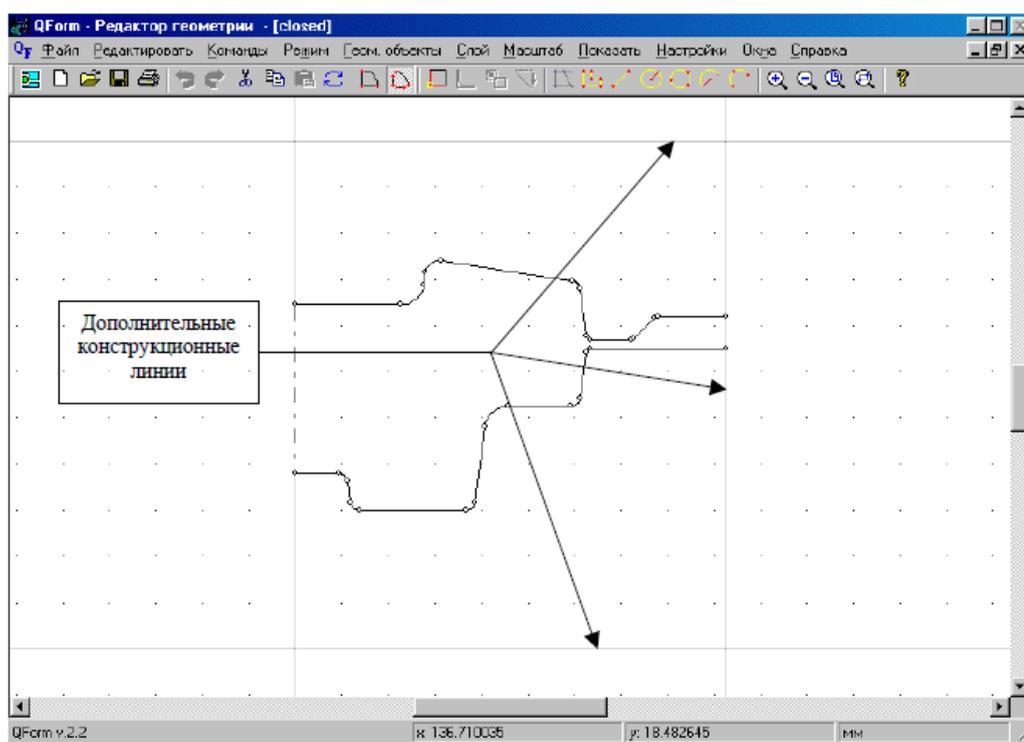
Чертеж с дополнительными конструкционными линиями для построения штамповых блоков
